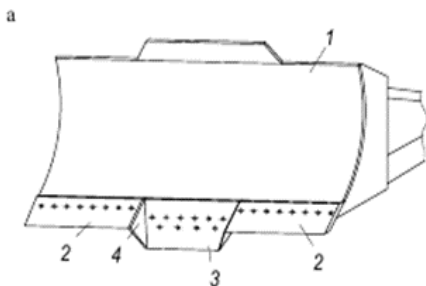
Рабочий орган бульдозера с ножом трапециевидной формы с зубьями на режущей кромке: 1 – отвальная поверхность; 2 – боковые ножи трапециевидной формы; 3 – средний выступающий нож трапециевидной формы; 4 – боковые косынки [2]
